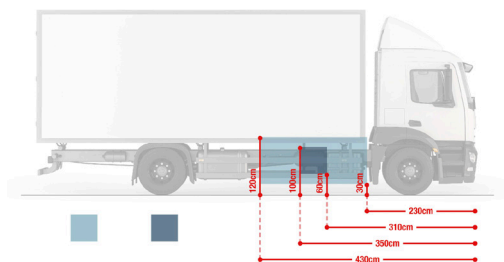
Schema di posizionamento consigliato o Plug&Play schema di posizionamento dell'installazione.
